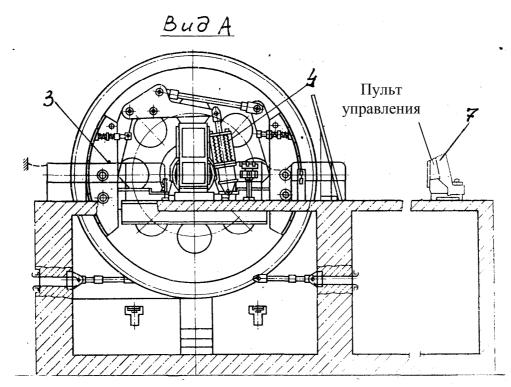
Подъемная машина типа МПБ с тормозом НКМЗ и внутренним расположением колодок: 1 — барабаны; 2 — соединительная муфта; 3 — тормозные колодки; 4 — пружинный безгрузовой привод тормоза; 5 — редуктор; 6 — электродвигатель; 7 — пульт управления
